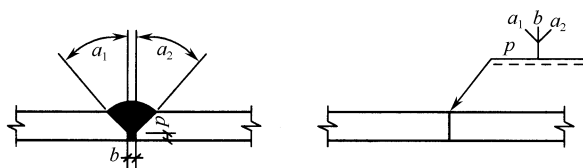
单面带双边不对称坡口焊缝的标注方法
